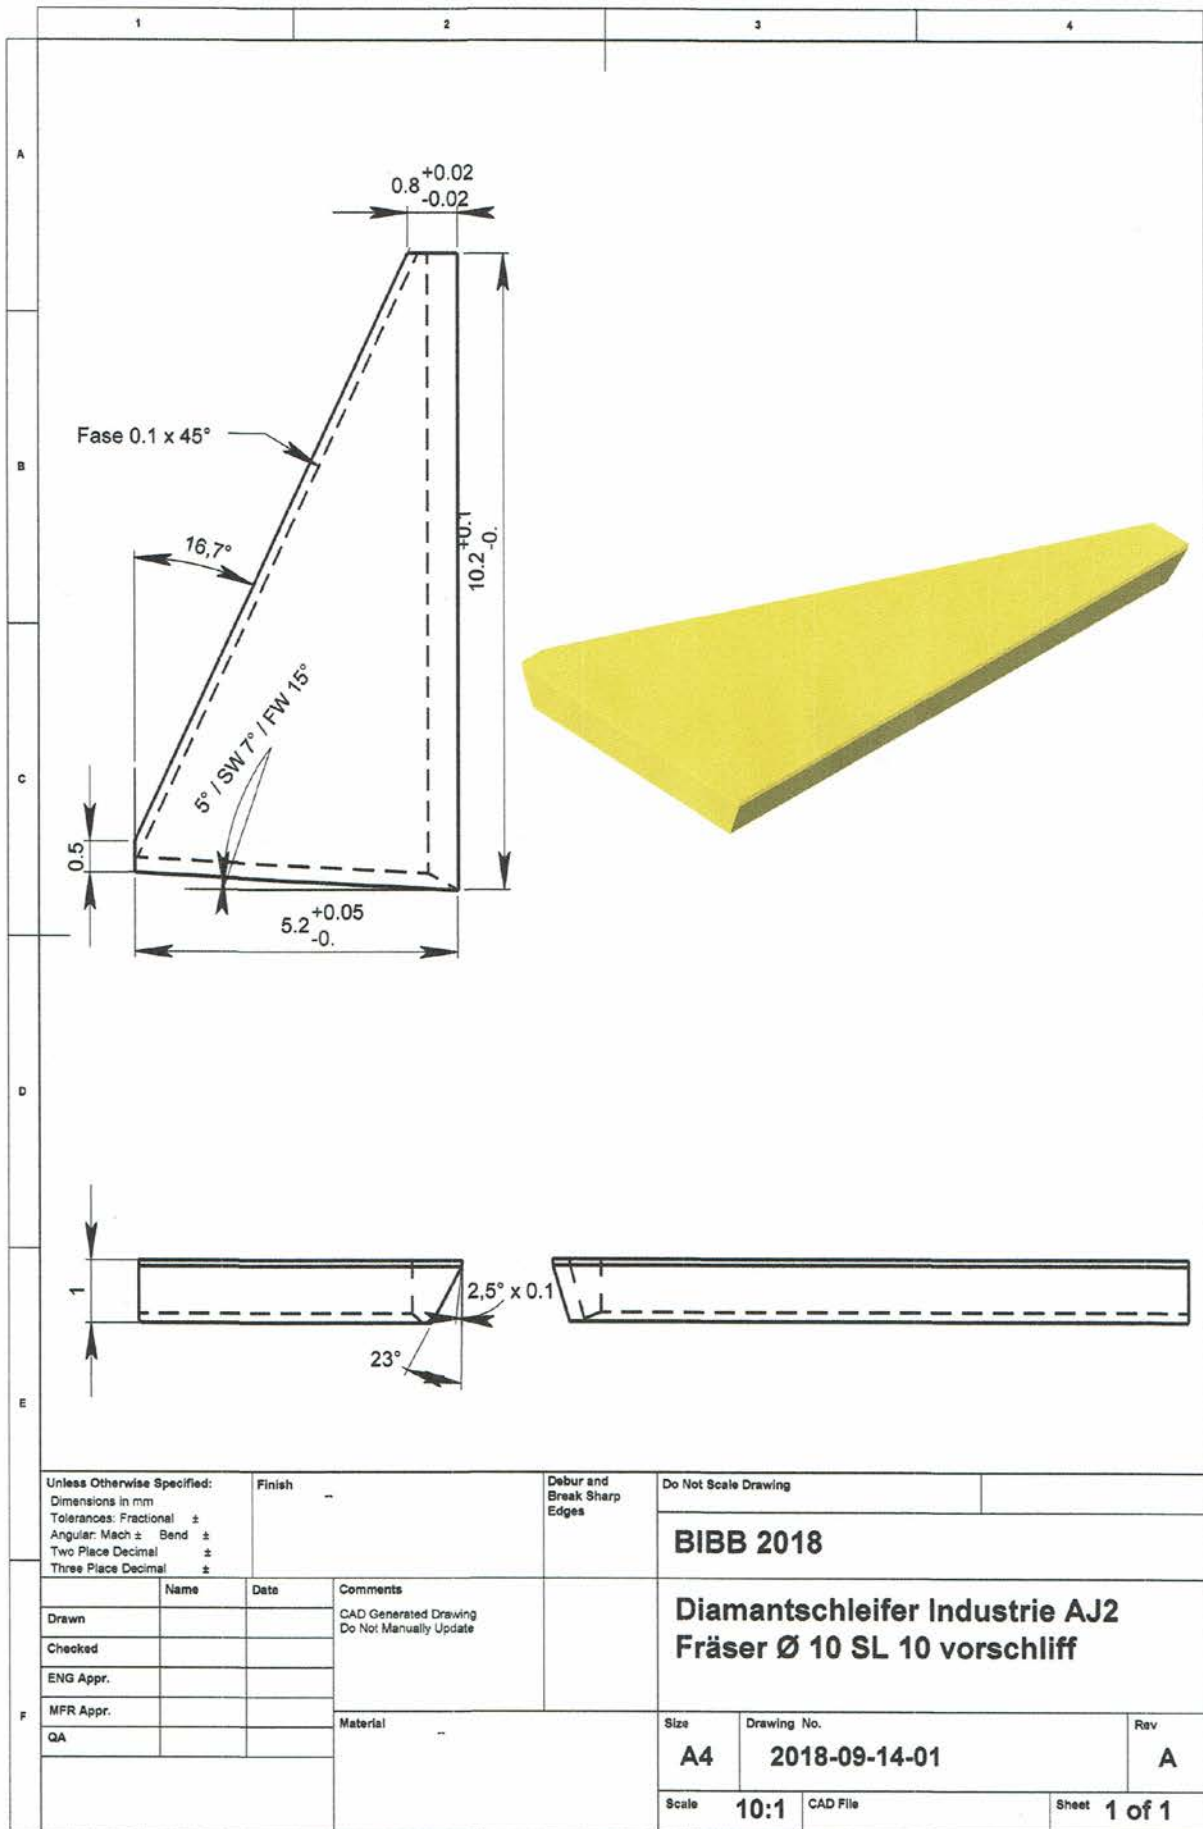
Diamantschleifer Industrie – Fräser (01)
